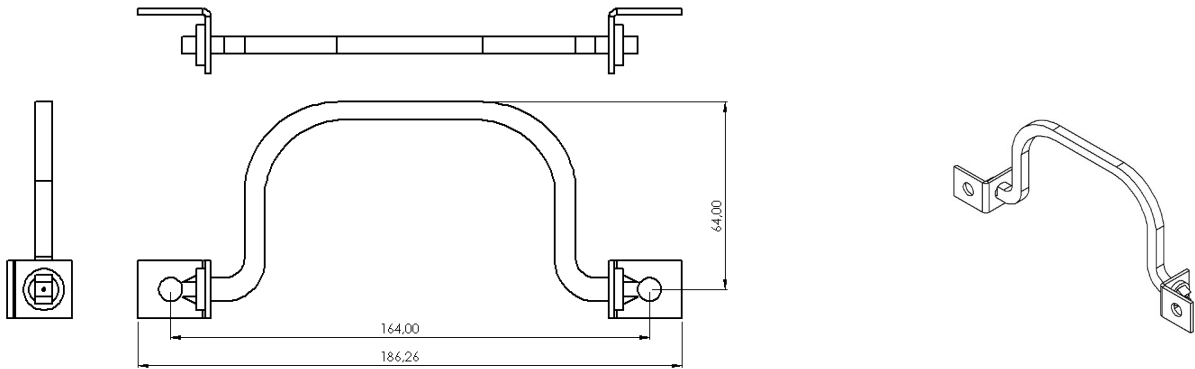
Σχέδιο πάνω βάσης στήριξης Part 2
